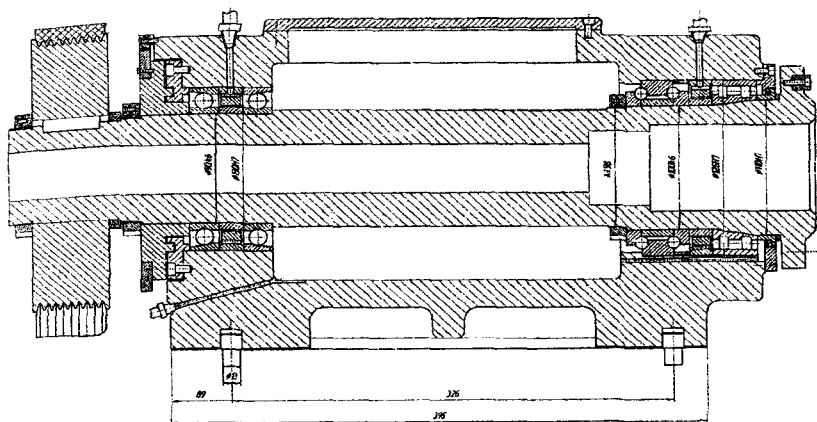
Автономная шпиндельная бабка горизонтального токарного станка со шпиндельным узлом в отдельном корпусе
